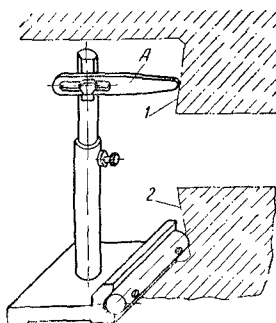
Приспособление для проверки соосности цилиндра и бабы.
